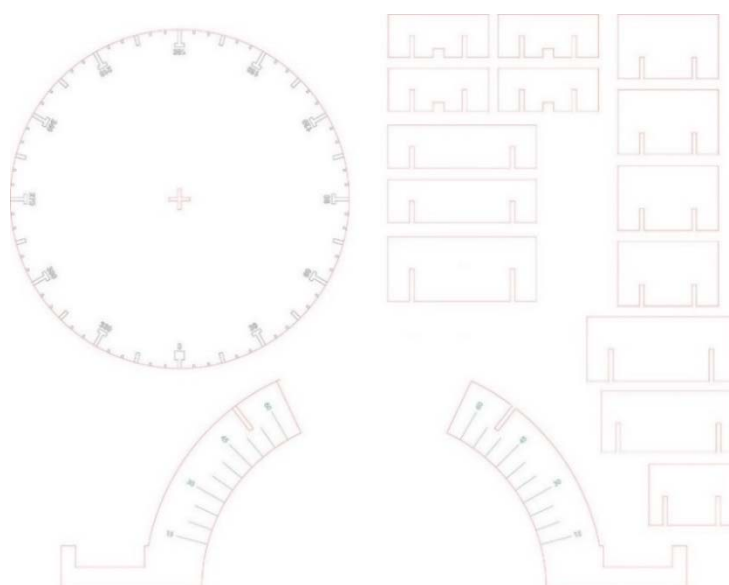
plan du dispositif adapté pour la découpeuse laser du FabLab de la HE-Arc Neuchâtel. Le tracé rouge correspond à la découpe, le tracé vert au marquage. © Porter, adapté par HE-Arc CR, RR
